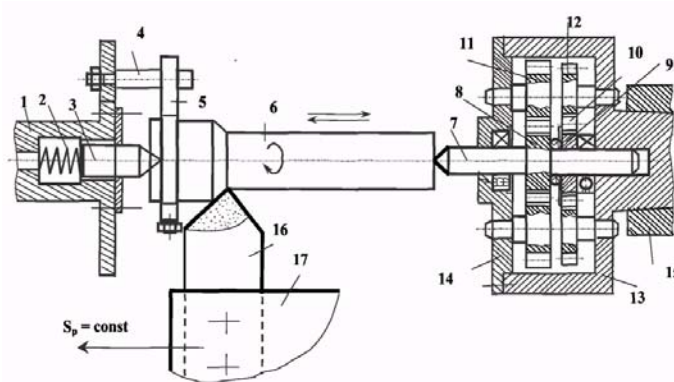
Пристрій для дроблення зливної стружки на токарному верстаті
